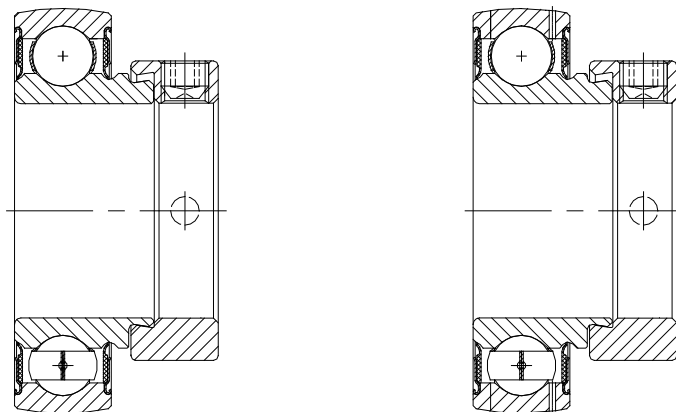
корпусные подшипники конструкций RAE и GRAE
